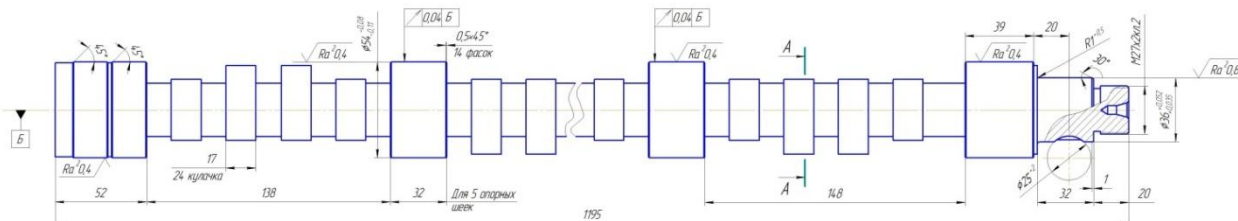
Чертеж распределительного вала двигателя ЯМЗ-240
